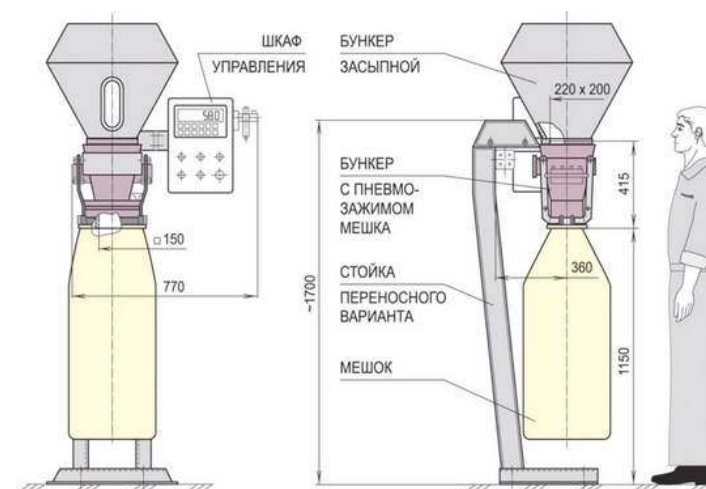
Общий вид дозатора фасовочного «Дора»
